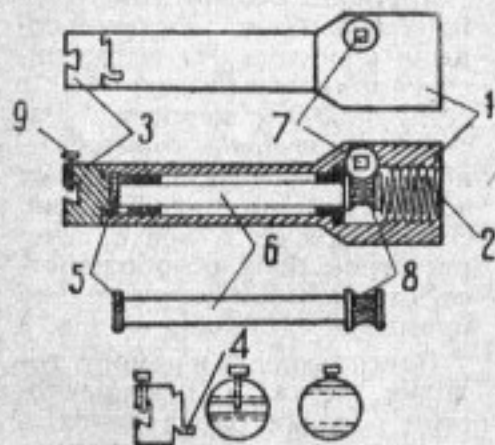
Приспособление для расточки цилиндров блока на токарном станке
